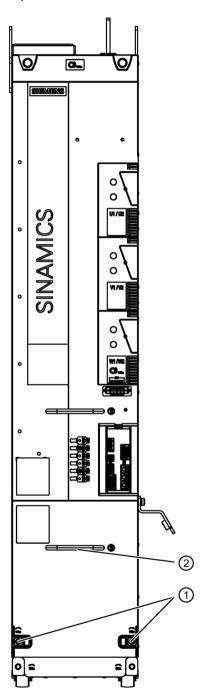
Замена вентилятора, модуль двигателя формата «шасси-2», типоразмер FS4
